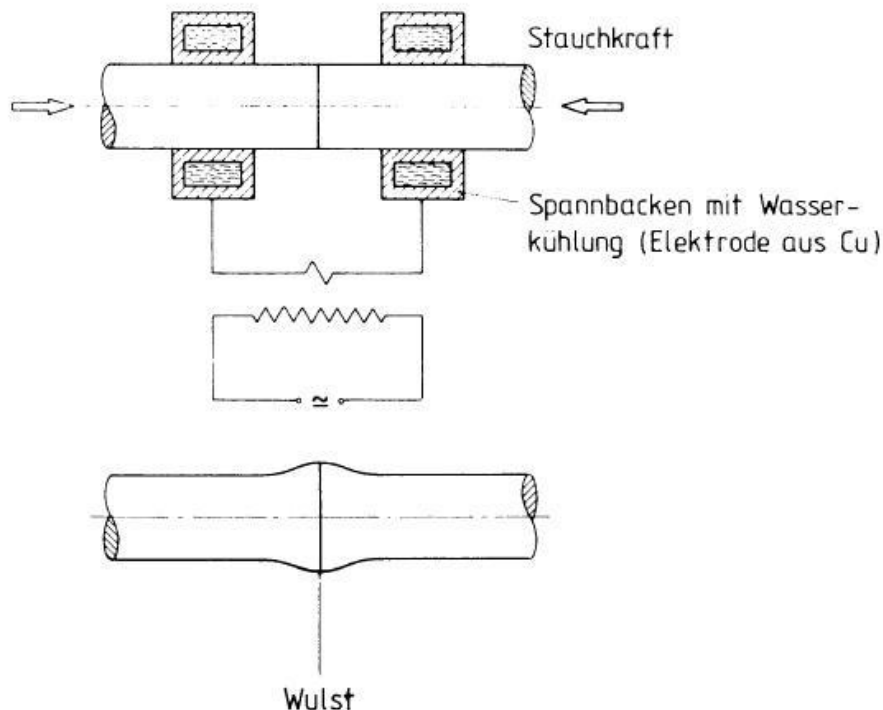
Verfahrensprinzip des Pressstumpfschweißens [30].
